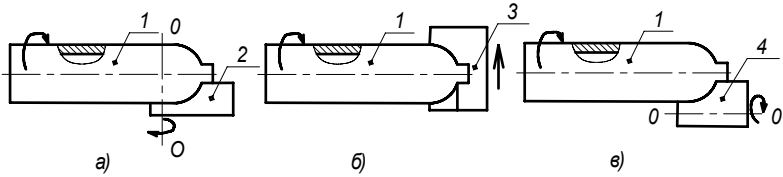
Схема обкочування трубчастих заготовок:
